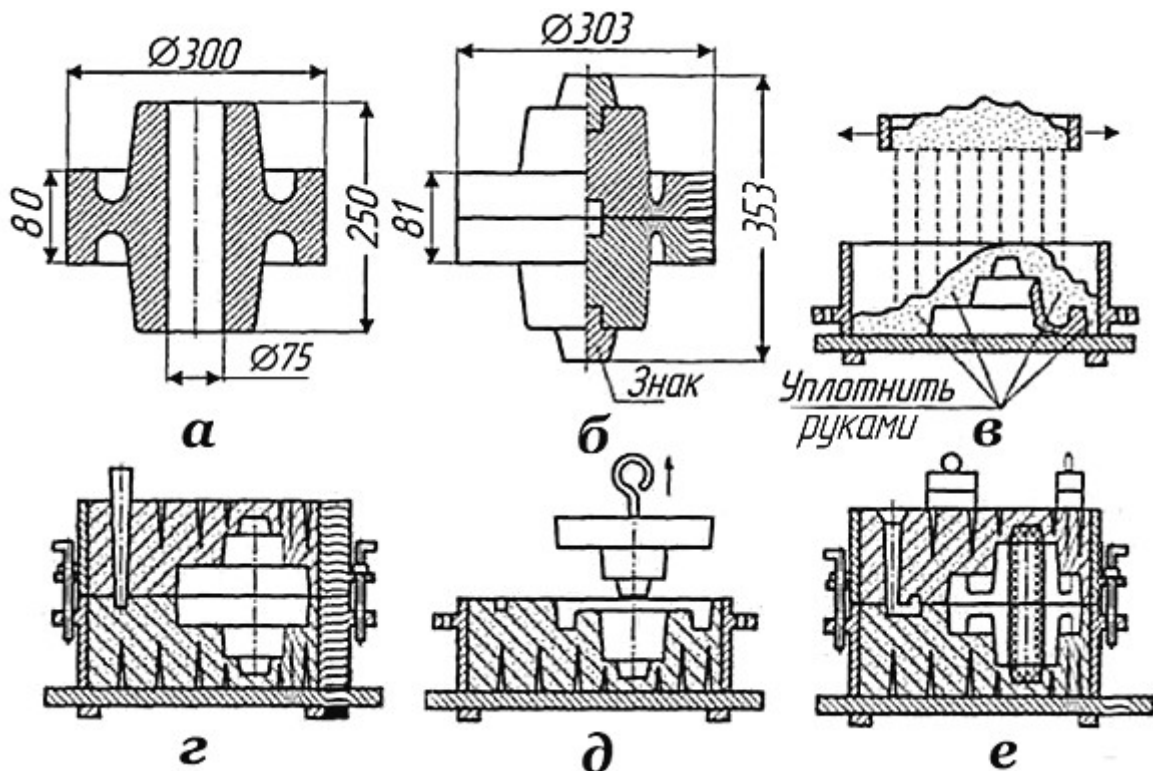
Формовка по разъемной модели: а – эскиз отливки; б – разъемная модель; в–е – операции формовки
